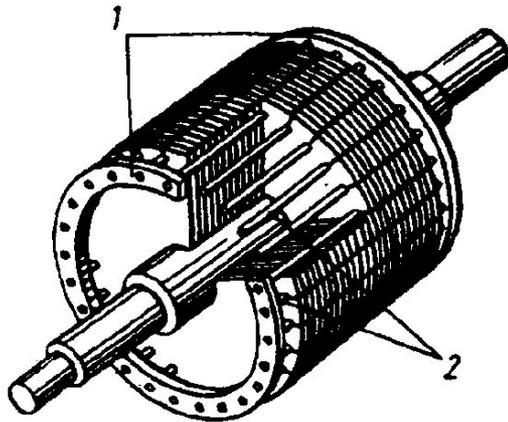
Короткозамкнутый ротор асинхронного двигателя со сварной обмоткой:
